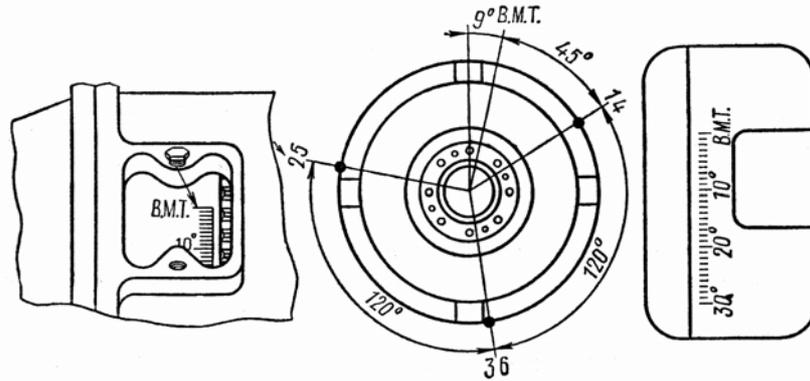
Вид на указатели и метки при регулировке клапанного механизма двигателя СМД-62
